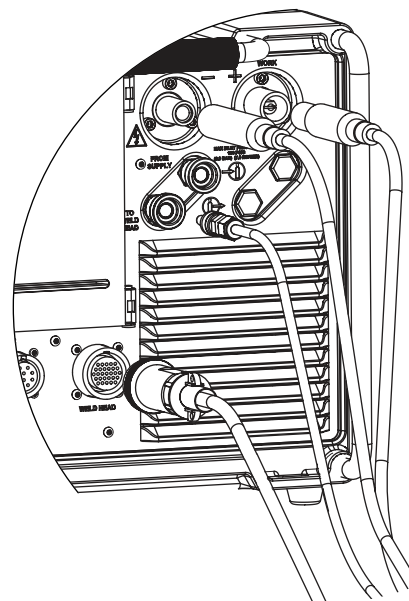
Connexion de la tête de soudure à l'unité d'alimentation
